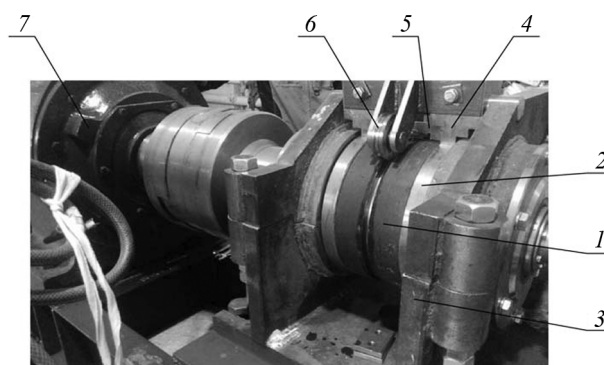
Прессовый узел установки Conform с новой системой крепления башмака
